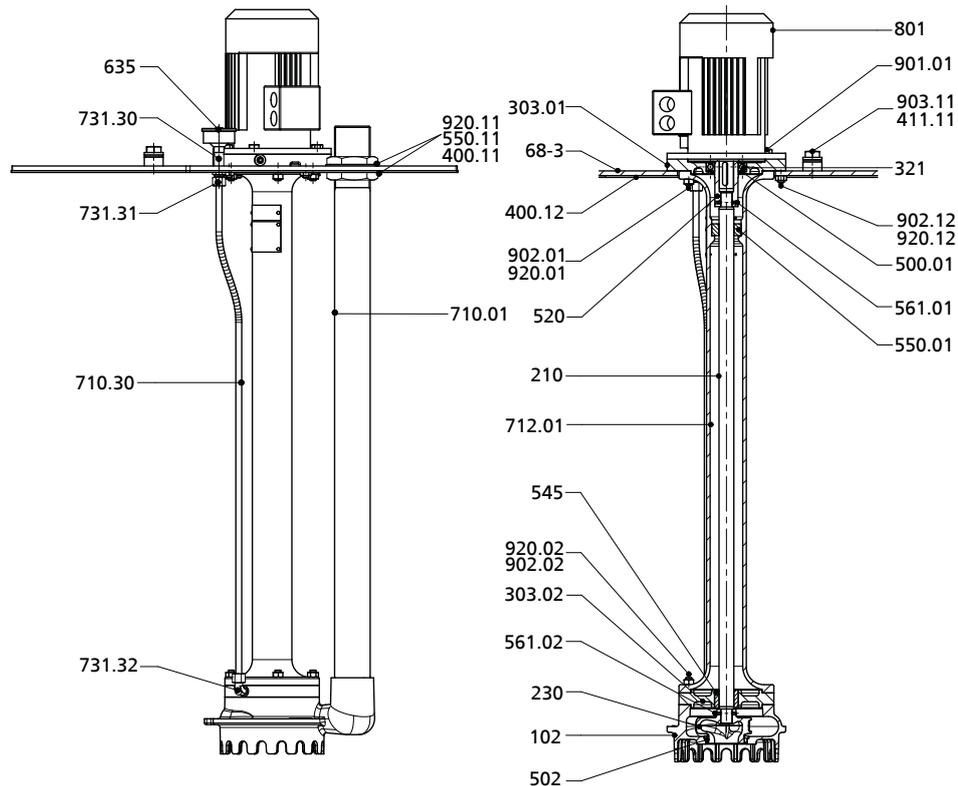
Чертеж МК, МКА - глубина установки 1000 мм - консистентная смазка
